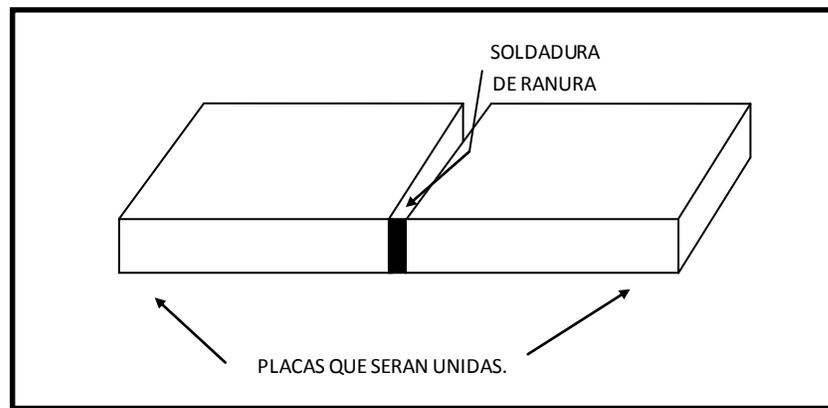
Placas unidas a tope con soldadura de ranura.
